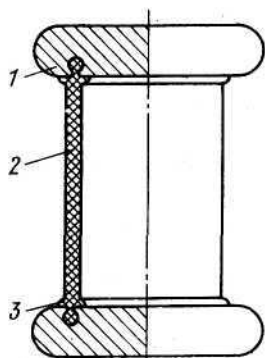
Соединение полиэтиленового тела трубчатого изолятора с металлической арматурой методом горячего формования
